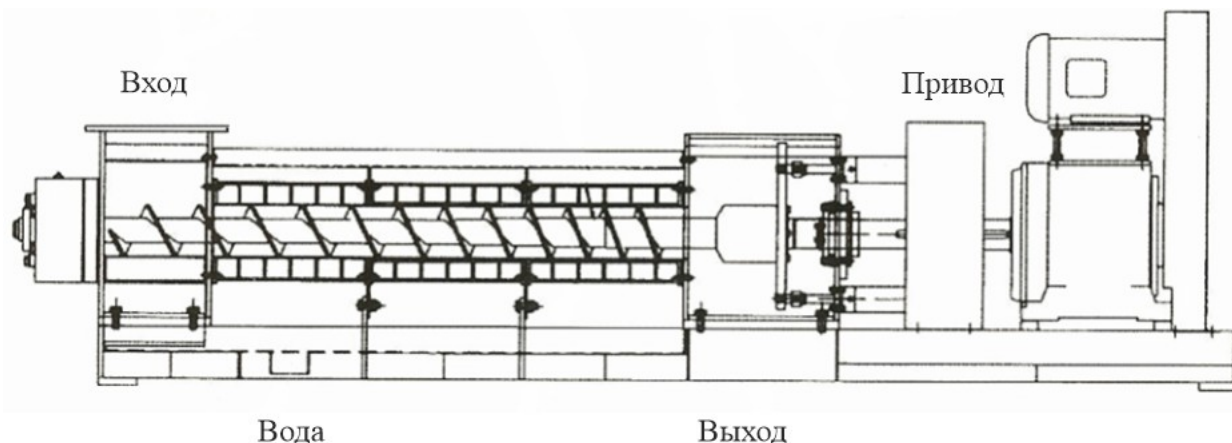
Шнековый пресс модели AGRI-PRESS
